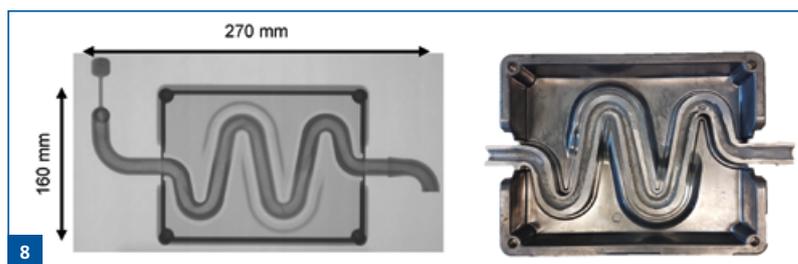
Kühlhäuse mit einem durch Gasinjektionstechnologie hergestellten Hohlkanal: (Kanaldurchmesser 10 mm, Kanallänge 420 mm): Röntgenaufnahme (links), Ansicht im Frähschnitt (rechts)
